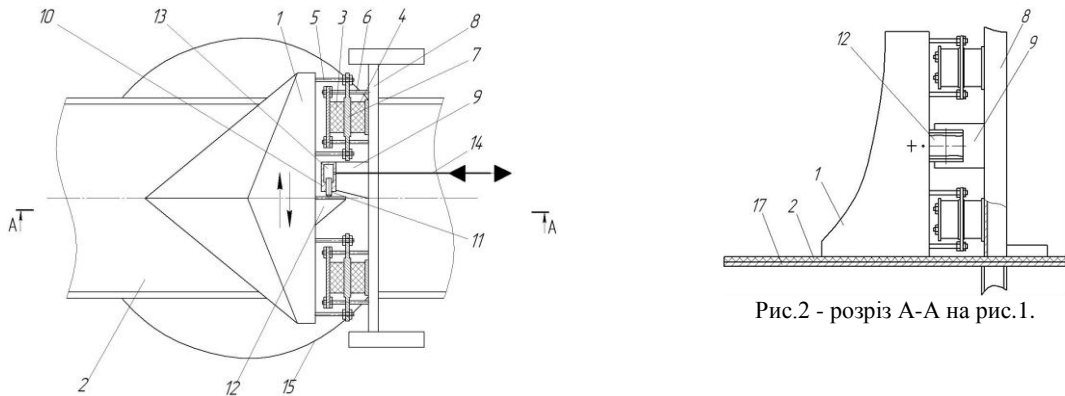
Конструктивне виконання плужкового вібраційного розвантажувача стрічкового транспортера (вид зверху)
